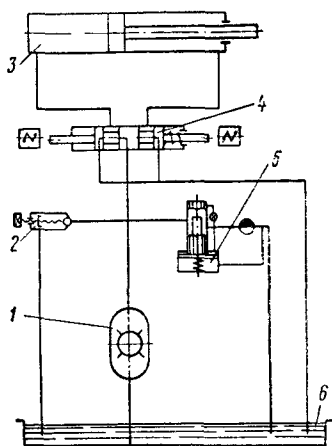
Схема гидравлического привода станка-автомата для выпрессовки текстолитовых клиньев:
